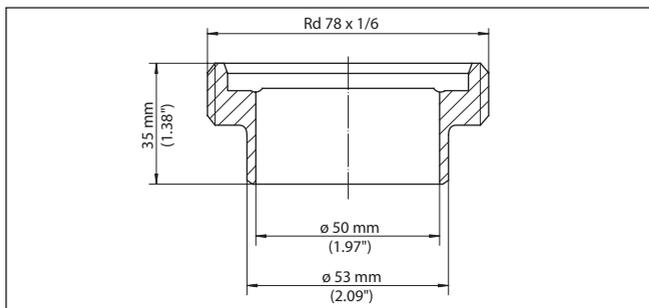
Dimensions raccord à souder raccord union DN 50 (DIN 1164-1)
